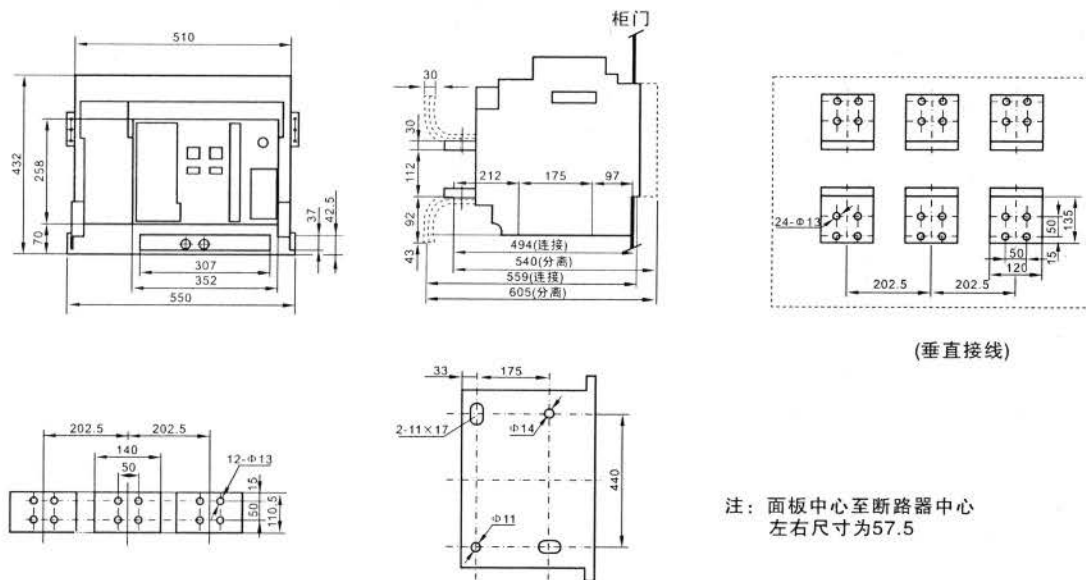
抽屜式断路器安装尺寸及外形尺寸(4000)
